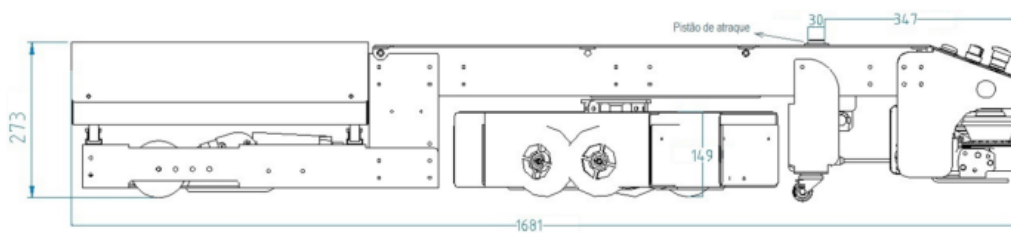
Dimensões [mm] críticas do AGV ASTI – EasyBot
